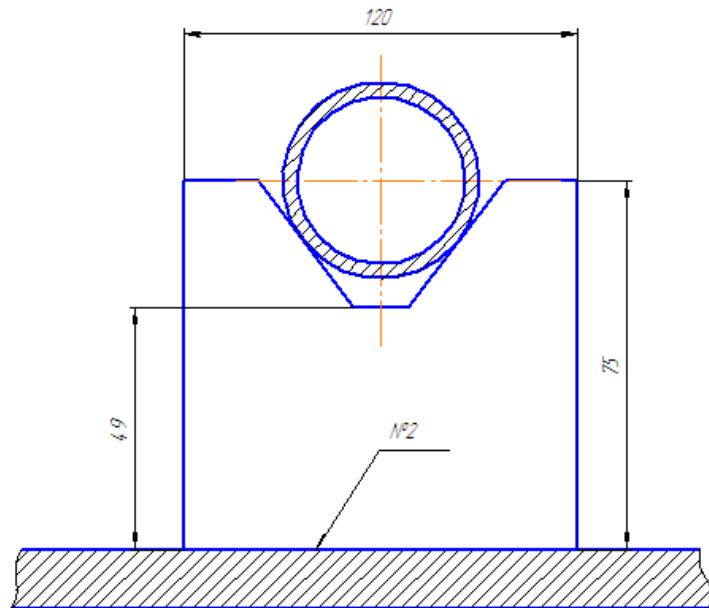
Базуюча площа трубчатого елемента зварної ферми
